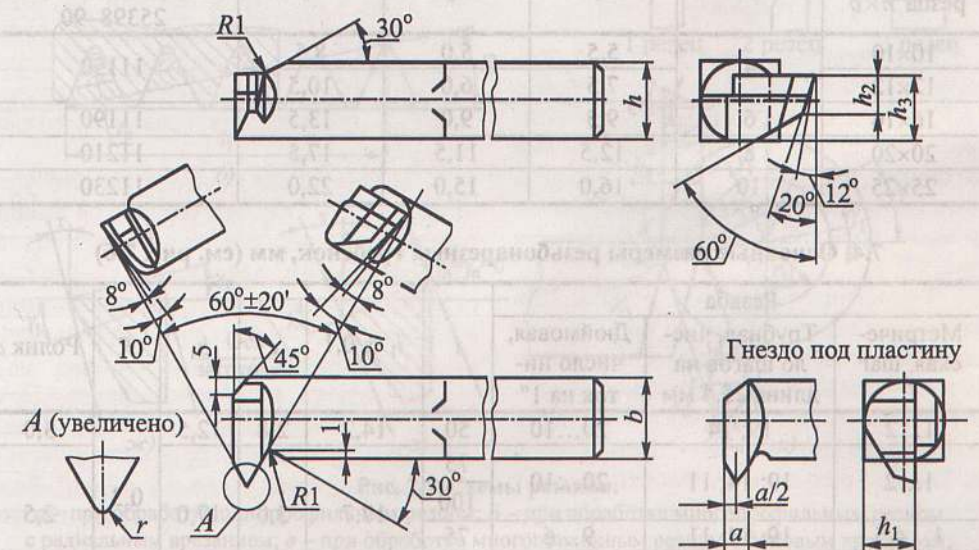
Размеры гнезда под твердосплавные пластины резцовых резцов для нарезания внутренних резьб
